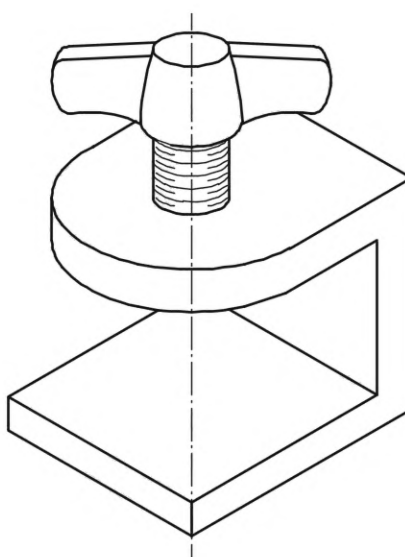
Винтовой зажим для изготовления образцов для испытания на прочность при сжатии
